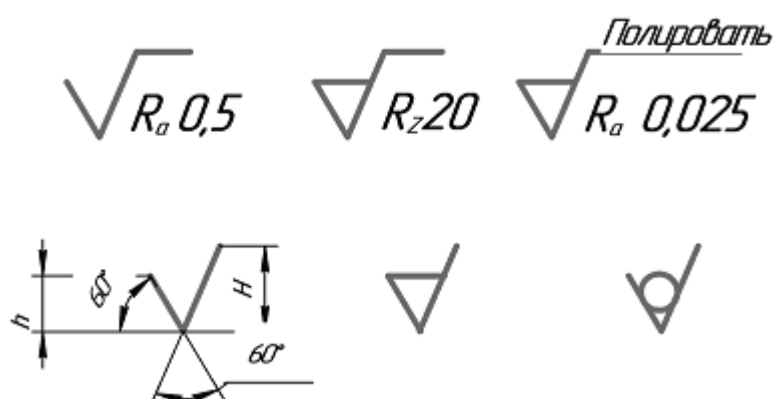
Обозначение и размеры знаков шероховатости поверхности
